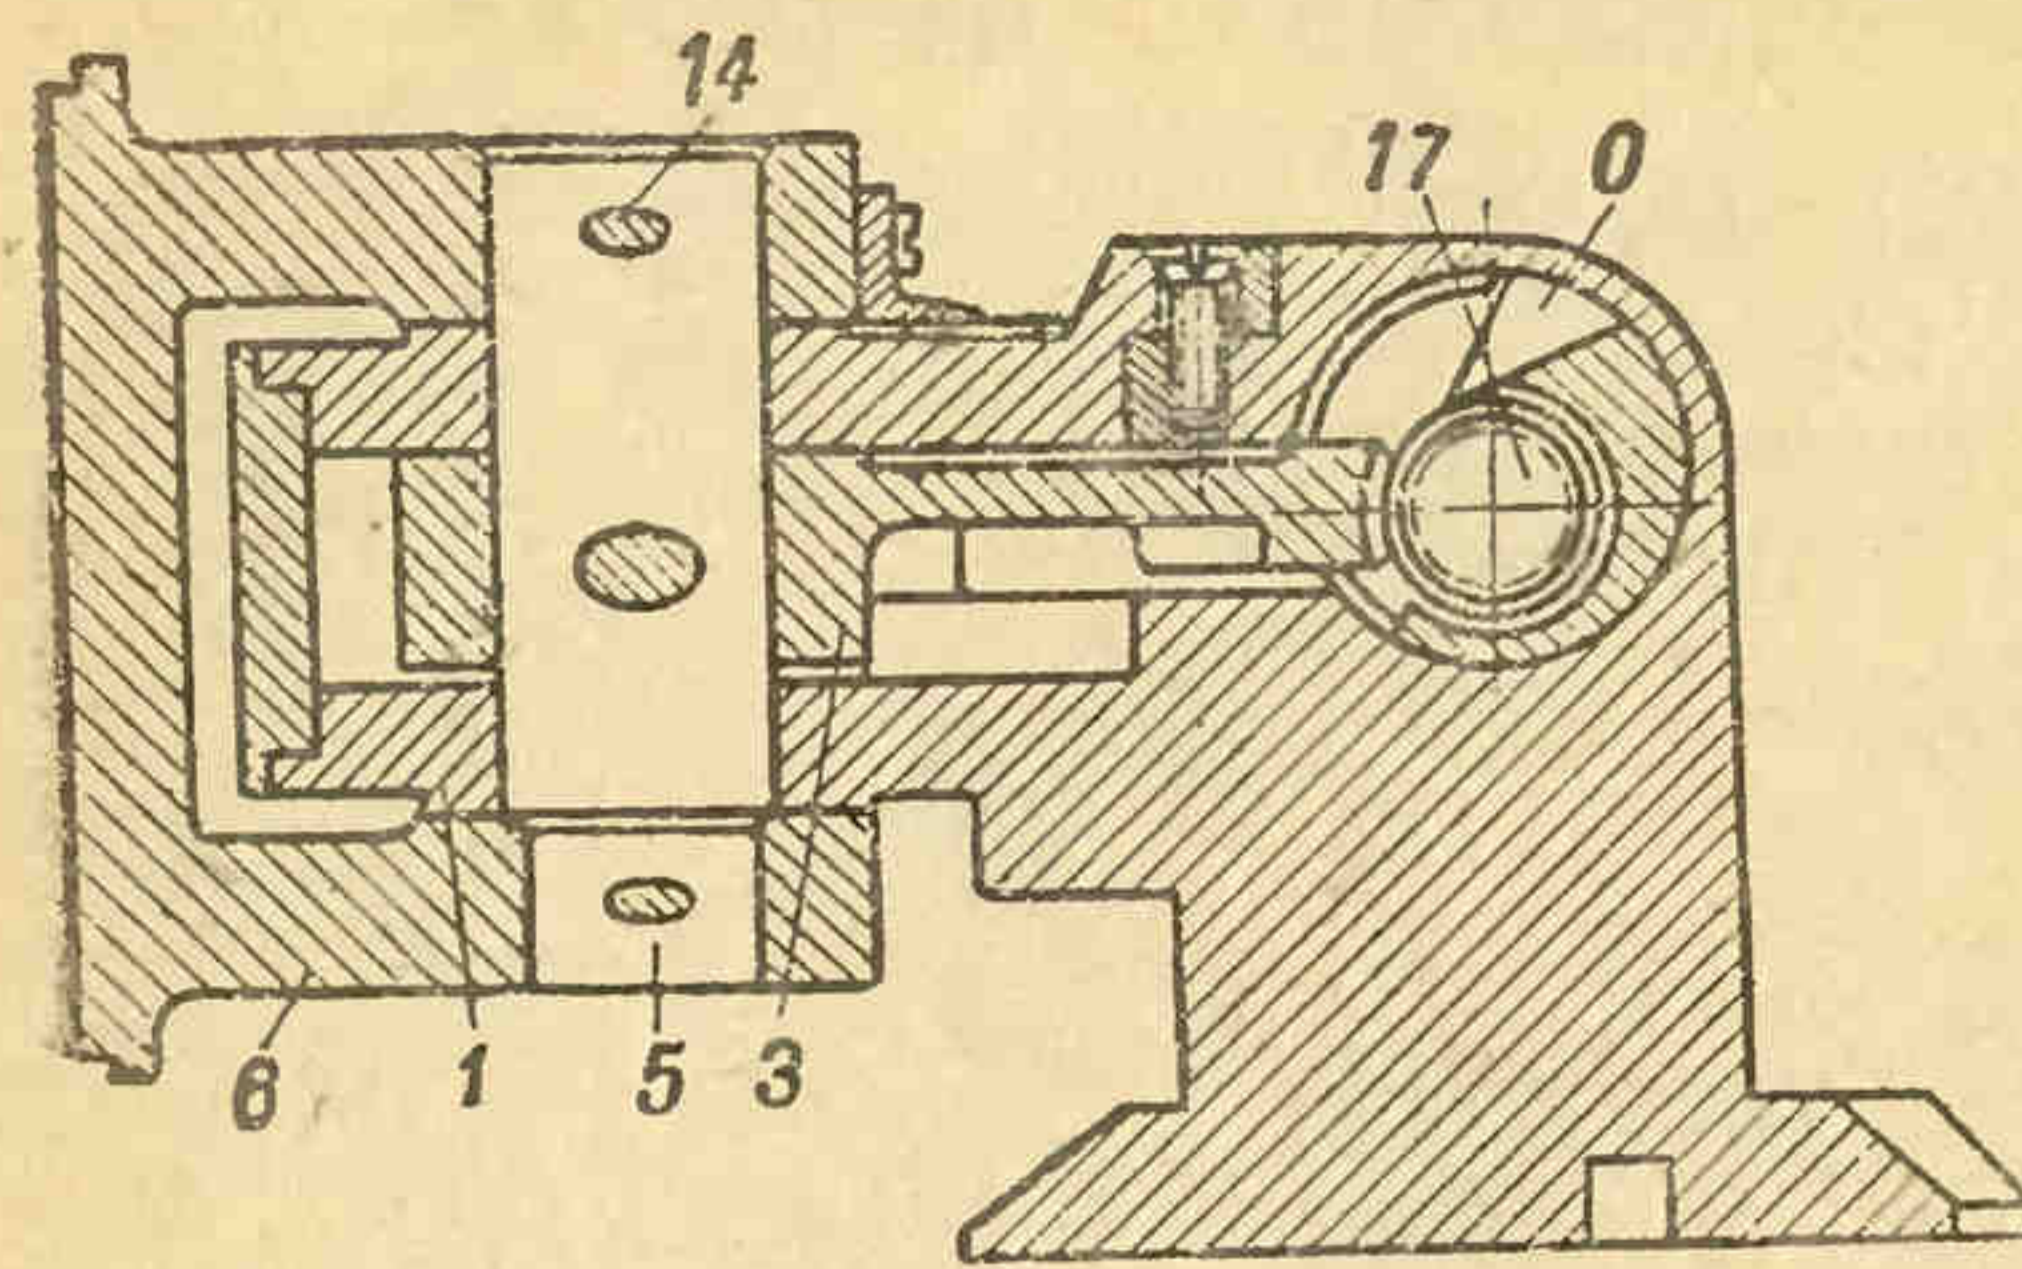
Механизм углов прицеливания: 1 — корпус механизма углов прицеливания; 2 — крышка; 3 — червячный сектор; 5 — ось червячного сектора (шарнир); 6 — кронштейн; 10 — эксцентриковая гайка; 14 — штифт; 15 — зажимная гайка; 16 — шайба червяка; 17 — червяк механизма углов прицеливания; 20 — пружина; 22 — эксцентриковый подшипник; 23 — пружинный подпятник; 24 — маховичок (кольцо); 25 — барабан с делениями; 0 — цилиндрическое отверстие.
